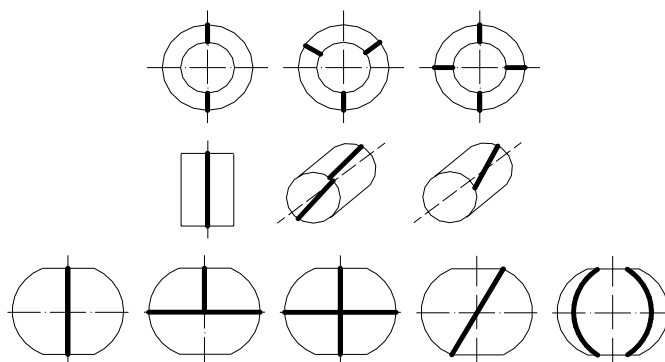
Варианты сварных заготовок и деталей «шар»
